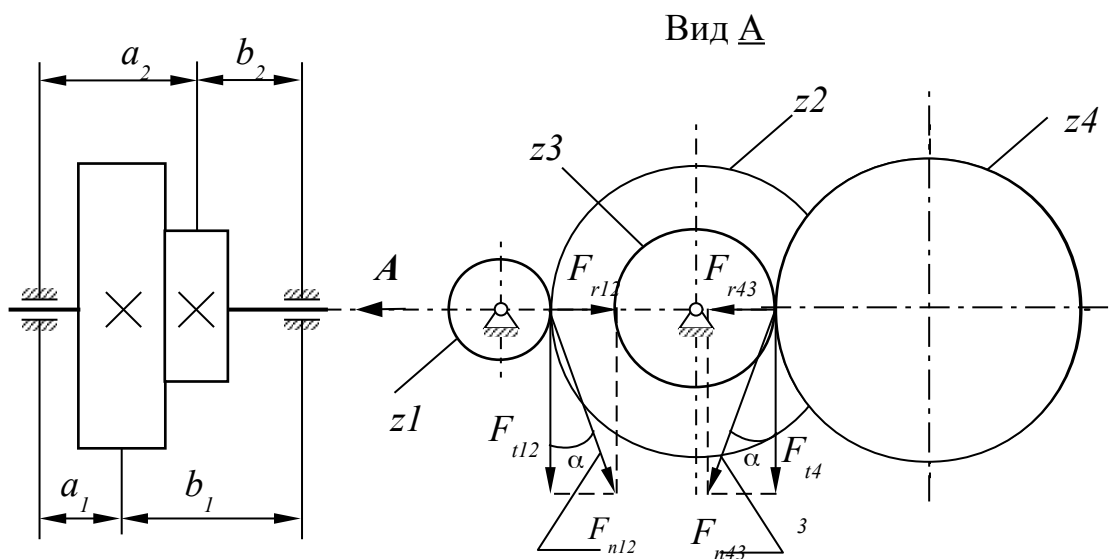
Схема проміжного вала та зусиль у зачепленні зубчастих коліс
